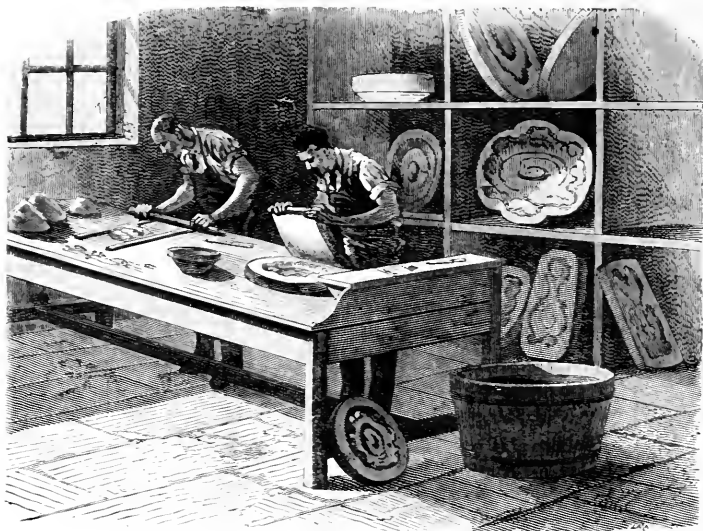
Façonnage d'une cuvette de porcelaine par le moulage à la croûte. (Dessin pris à la manufacture de Sèvres.)
